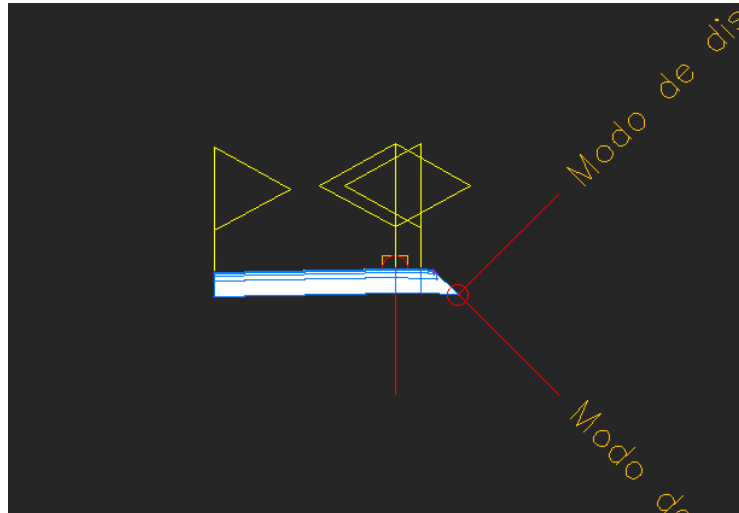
Ensamblaje patas glorieta. Fuente: Elaboración propia.
